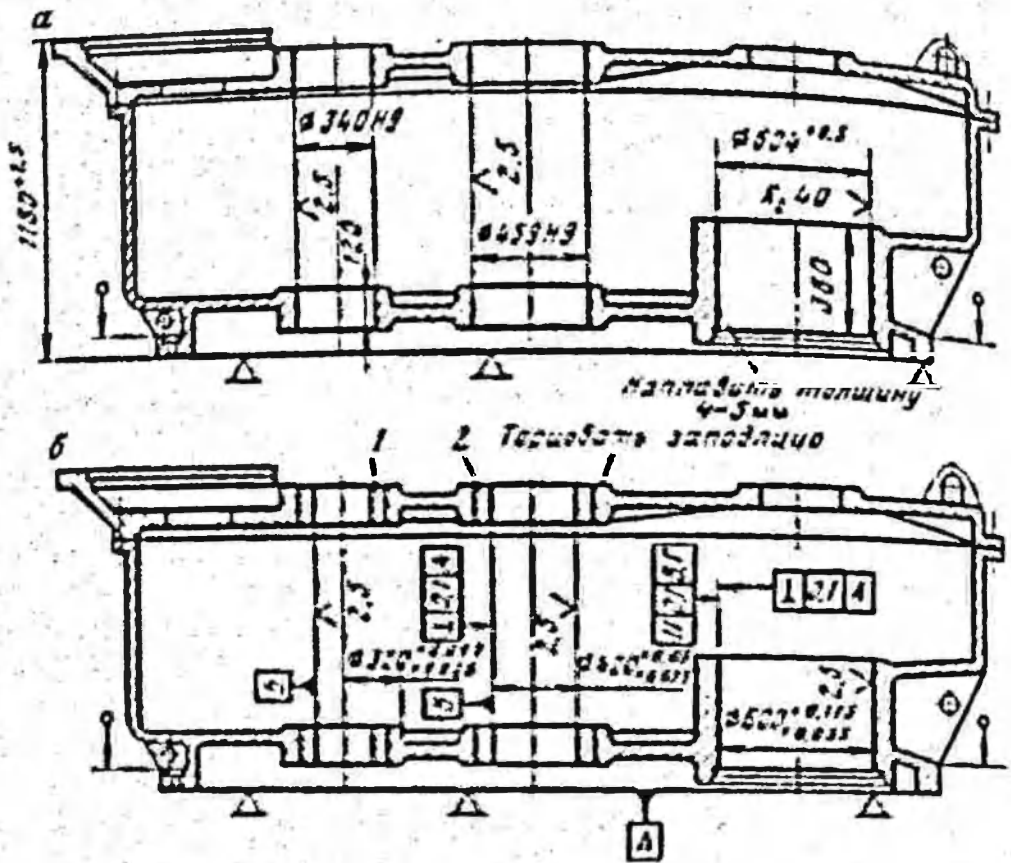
Ремонтные чертежи корпуса и вращающ. редуктора поворотного механизма экскаватора ЭШ-10/70А после предварительной расточки отверстий (а) и запрессовки втулок и чистовой расточки отверстий (б)
